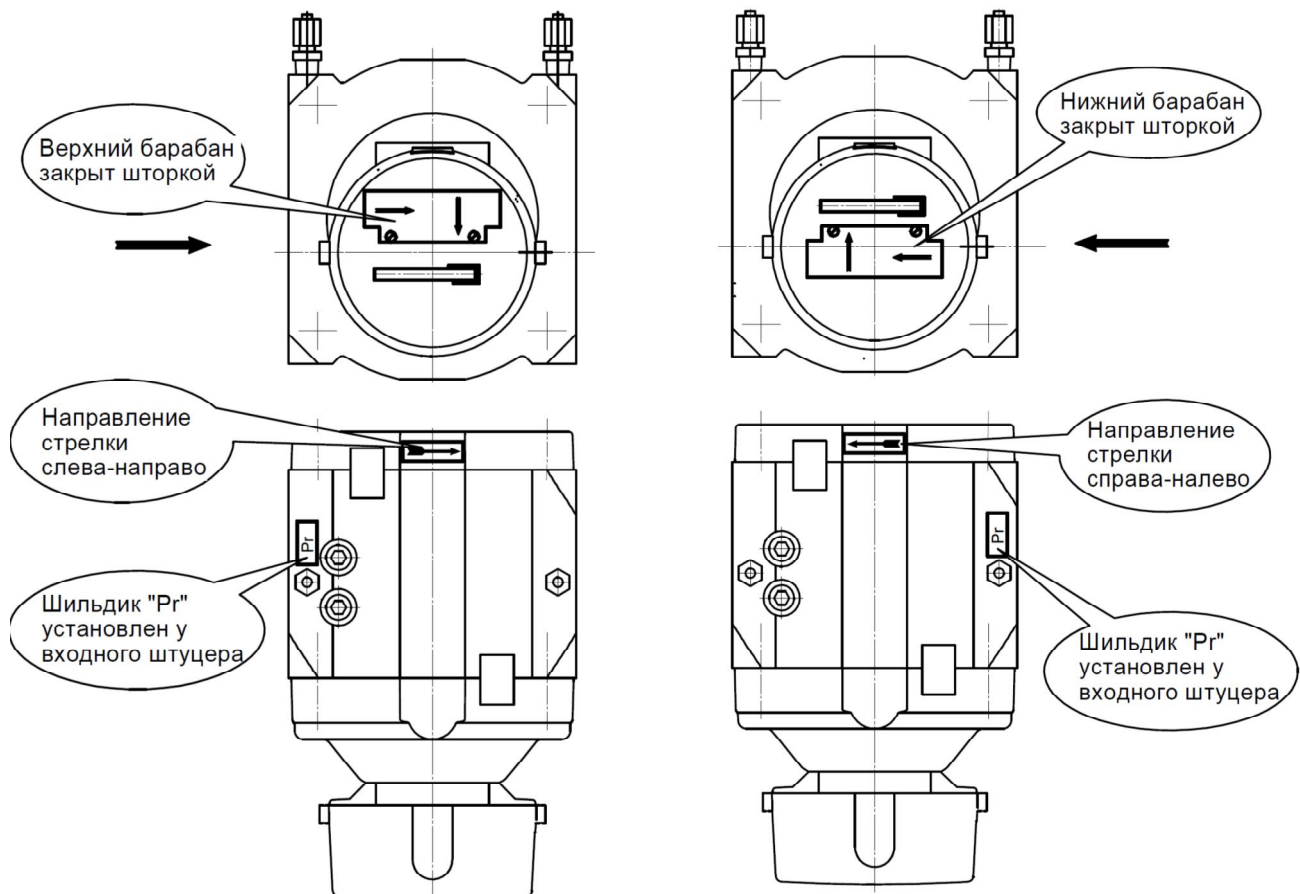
Установка шторки и шильдиков при направлении потока газа слева-направо.
